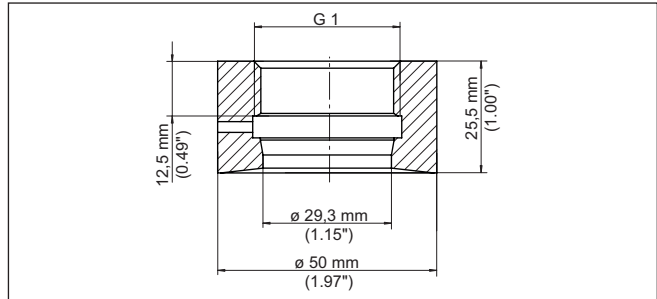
Maße Direkt-Einschweißstutzen G1 (ISO 228-1) - O-Ring-Dichtung
